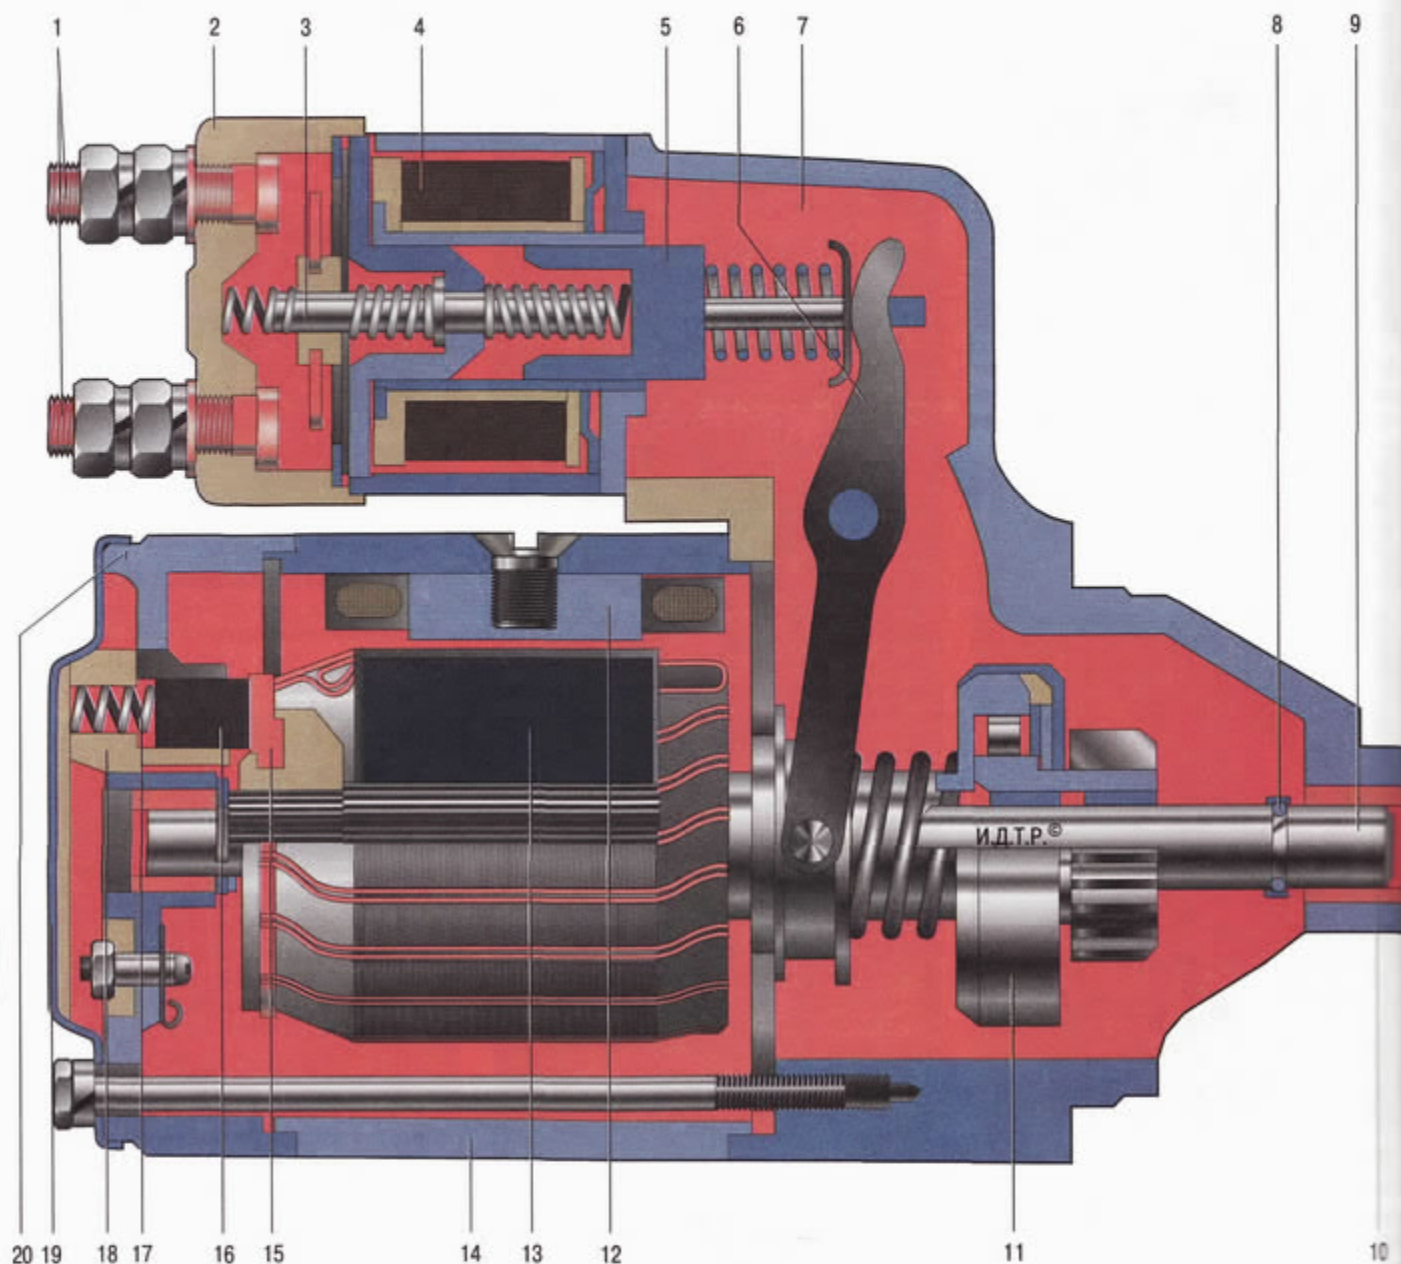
Стартер 265.3708: 1 – контактные болты; 2 – крышка реле; 3 – шток тягового реле; 4 – обмотка реле; 5 – якорь тягового реле; 6 – рычаг привода; 7 – крышка со стороны привода; 8 – ограничительное кольцо хода шестерни; 9 – вал якоря; 10 – втулка якоря; 11 – обгонная муфта; 12 – полюс статора; 13 – якорь; 14 – корпус статора; 15 – коллектор; 16 – изолированная щетка; 17 – пружина щетки; 18 – щеткодержатель; 19 – крышка коллектора; 20 – крышка со стороны коллектора
